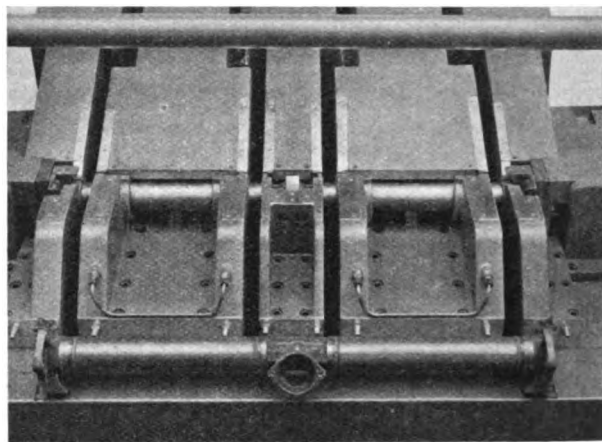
Einspannvorrichtung für die gleichzeitige Mehrstellenschweißung.
